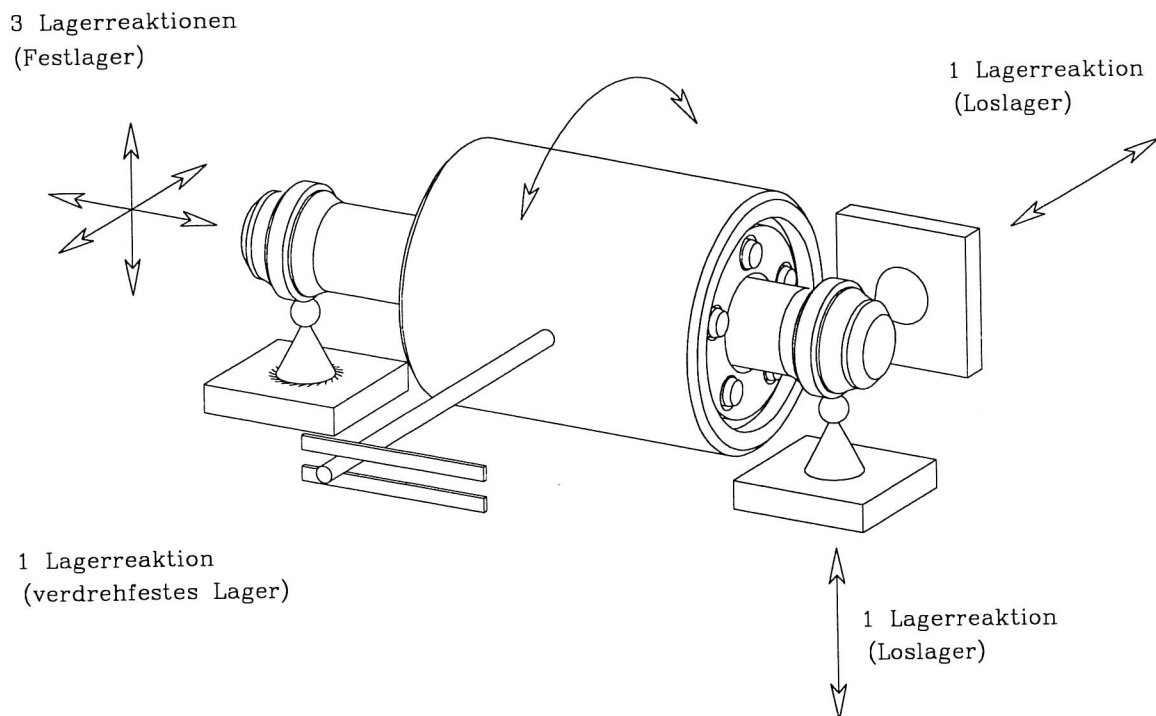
Lagerreaktionen bei statisch bestimmter Lagerung
